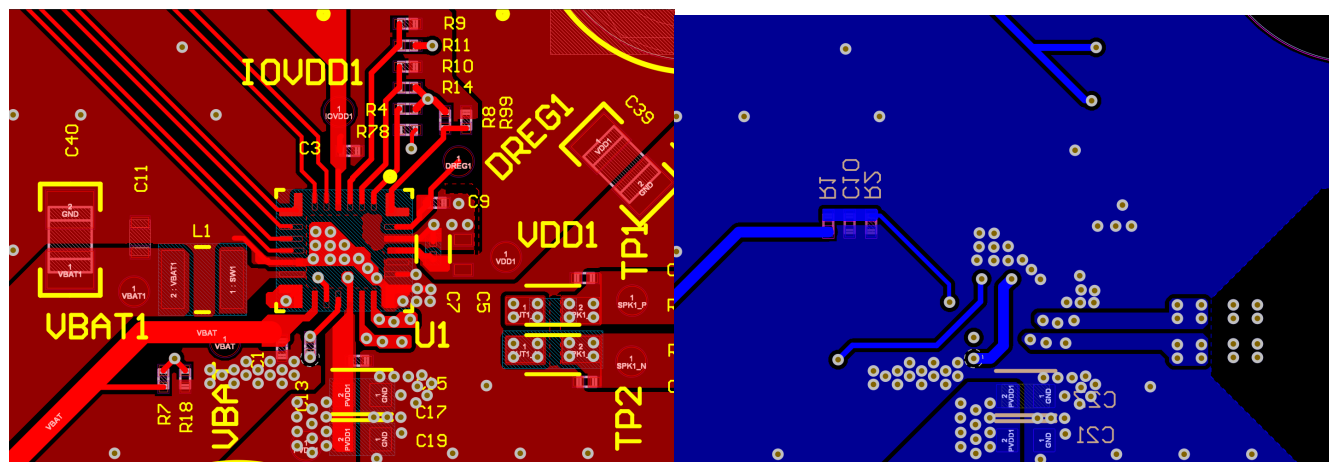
顶层 (红色) 和底层 (蓝色) — 硬件控制参考 PCB 布局
